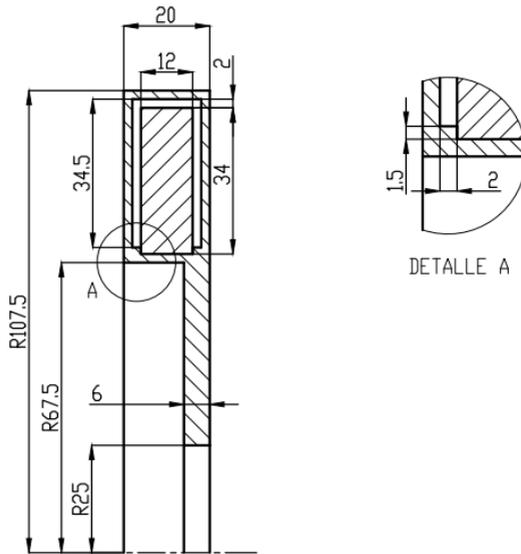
Vista en corte con dimensiones del amortiguador, solamente se muestra la mitad por ser componente de revolución, fuente propia.
